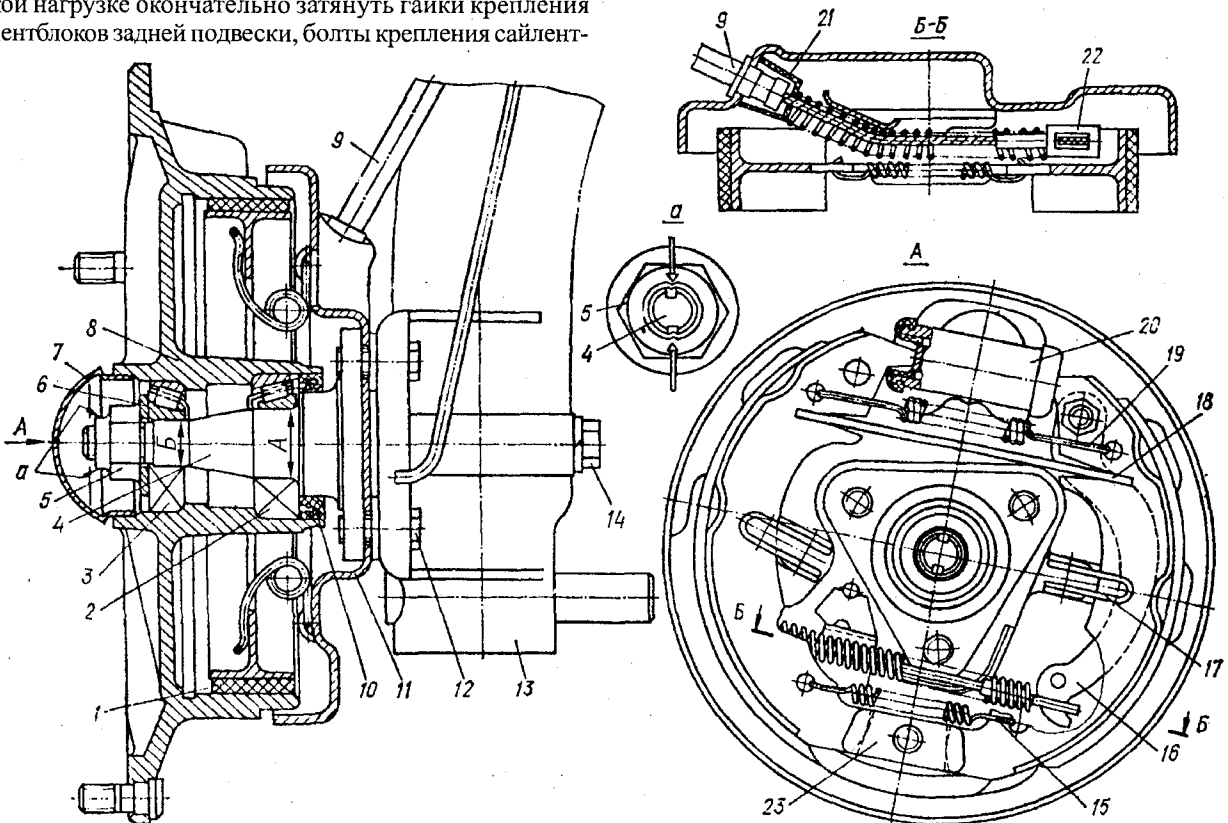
Задняя подвеска и задний тормоз со ступицей и подшипниками: 1 – колодка тормоза; 2 – подшипник внутренний; 3 – подшипник наружный; 4 – ступица; 5 – гайка ступицы; 6 – шайба запорная; 7 – колпак; 8 – тормозной барабан; 9 – трос стояночного тормоза; 10 – сальник; 11 – щит тормоза; 12 – болт крепления ступицы (короткий); 13 – балка задней подвески; 14 – болт крепления ступицы (длинный); 15 – пружина стяжная нижняя; 16 – рычаг разжимной; 17 – пружина колодок; 18 – планка распорная; 19 – пружина стяжная верхняя; 20 – цилиндр колесный; 21 – упор троса; 22 – наконечник троса; 23 – опора колодок; вид А – тормоз задний без барабана; а – стопорение гайки 5 путем вдавливания юбки гайки в пазы на конце вала ступицы 4
